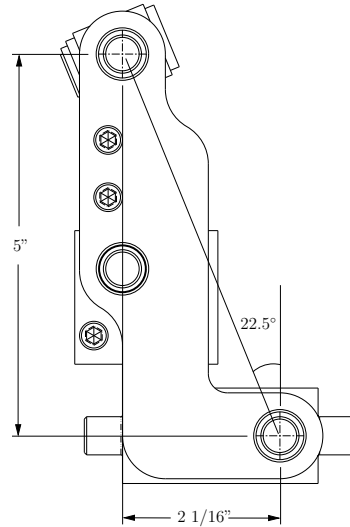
Nouvelles dimensions de la patte du mécanisme de positionnement.
